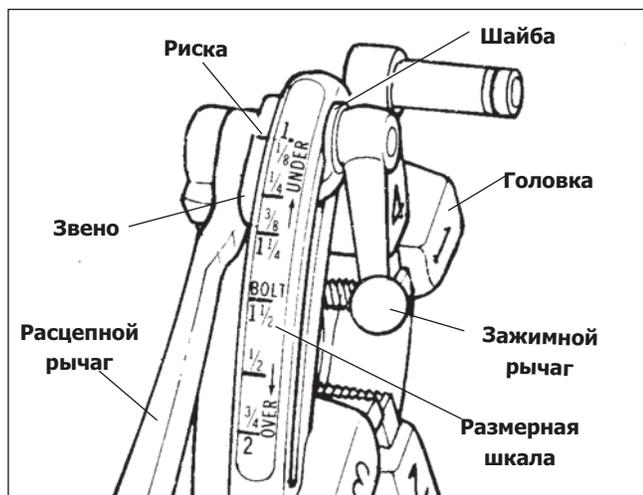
Универсальная быстрооткрывающаяся головка
